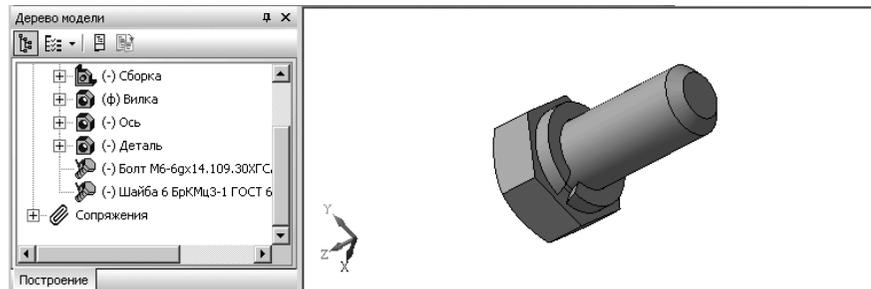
Результат сборки стандартных изделий – болта с шайбой
